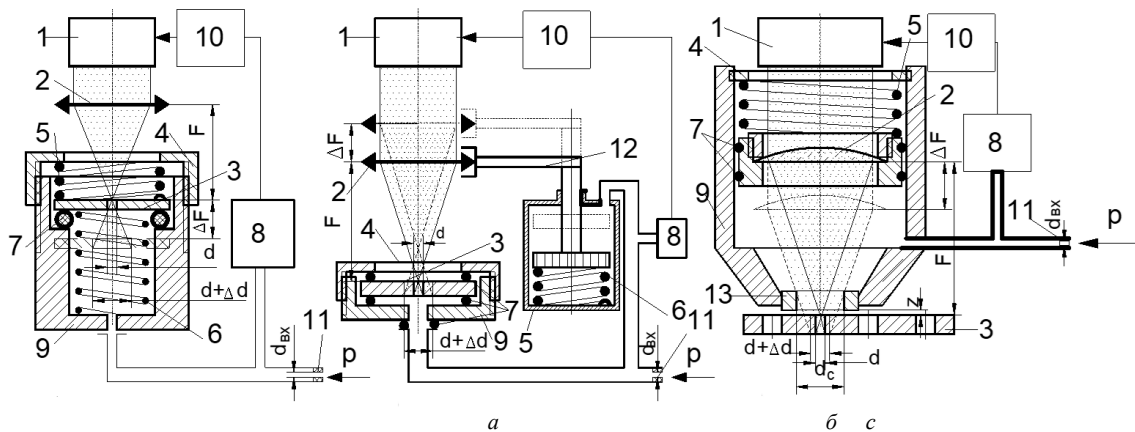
Схеми пристосувань для реалізації технологічних операцій обробки отворів з адаптивною організацією, (*a* – обробка отворів в тонких заготовках простої форми з одним отвором; *b* – в заготовках будь-якої форми з одним отвором; *в* – в листових заготовках з будь-якою кількістю отворів), (*a*: 1 – лазер, 2 – об’єктив, 3 – заготовка, 4 – кришка камери, 5, 6 – пружини, 7 – ущільнення, 8 – чутник тиску, 9 – корпус вимірювальної камери, 10 – процесор, 11 – вхідна діафрагма; *b*: 5 – пневмоциліндр, 12 – важіль; *в*: 4 – пружна шайба, 12 – сопло
